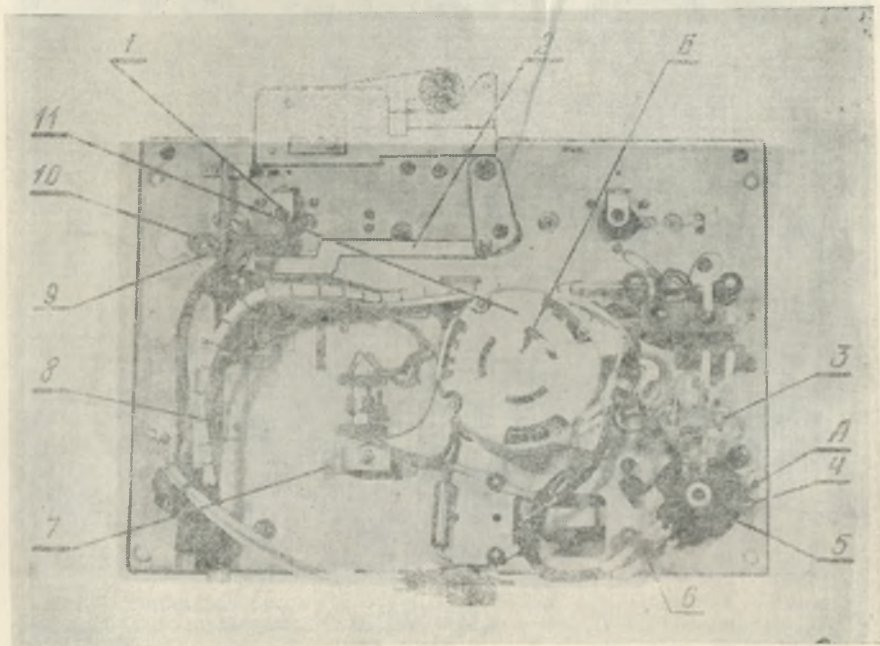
Лентопротяжный механизм. (Вид снизу):
